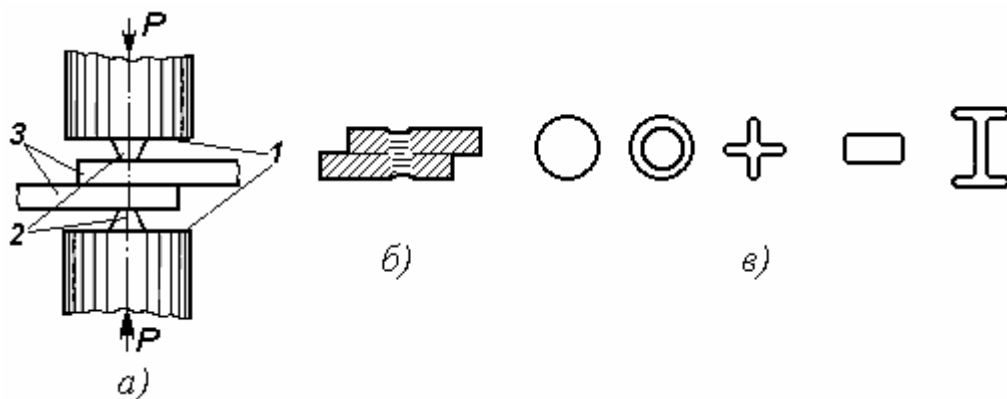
Холодная сварка: а) схема точечной сварки; б) сварное соединение; в) формы сварных точек
